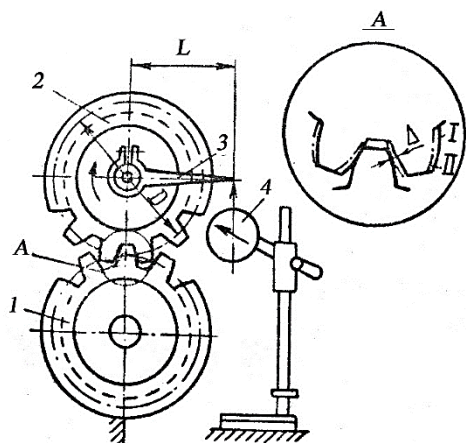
Контроль бокового зазору в зачепленні циліндричних зубчастих коліс:
